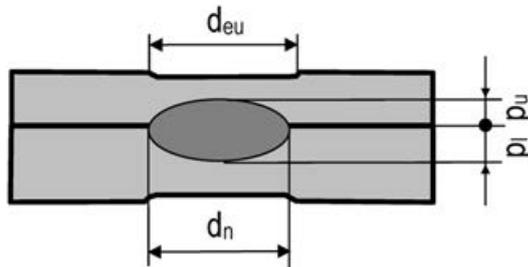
Größen zum Erfassen von Form und Ausdehnung einer Punktschweißverbindung mit unterschiedlicher Blechdicke (einschnittig).
